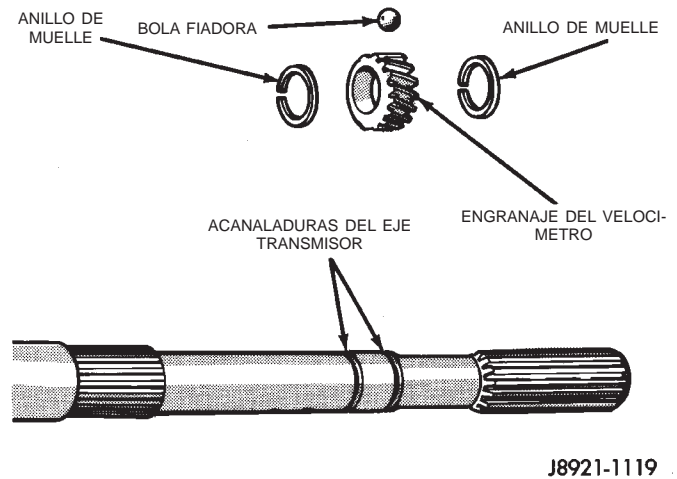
Conjunto de engranaje propulsor del velocímetro
